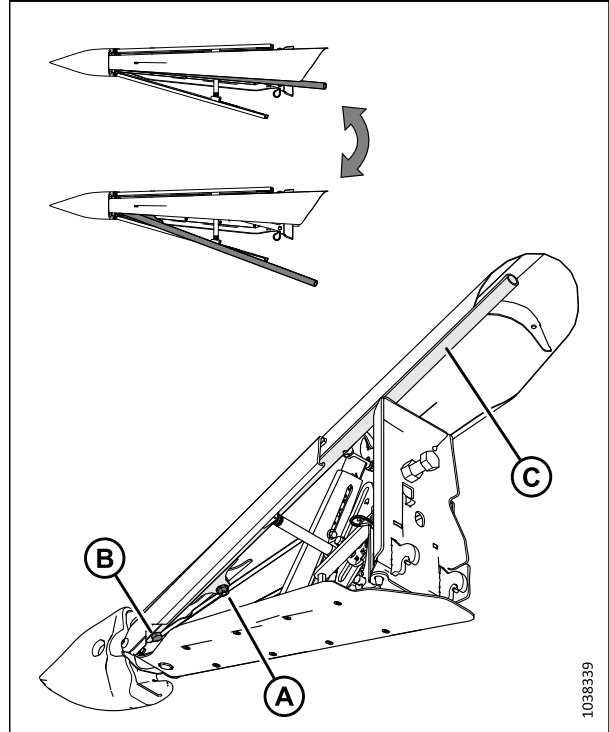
Регулировка бокового стержня верхнего дефлектора
